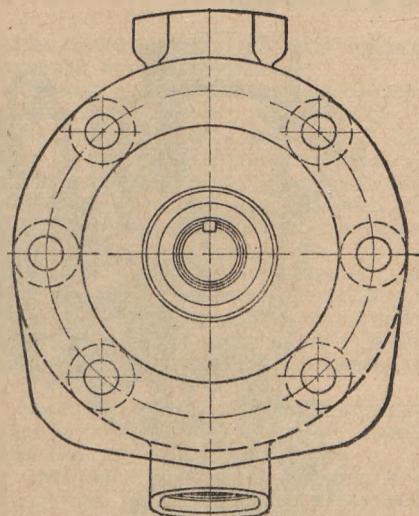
Фланец усиленного поворотного кулака автомобиля ГАЗ-51.
